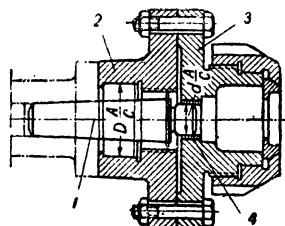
Установка приспособления с помощью центрирующего пальца.
